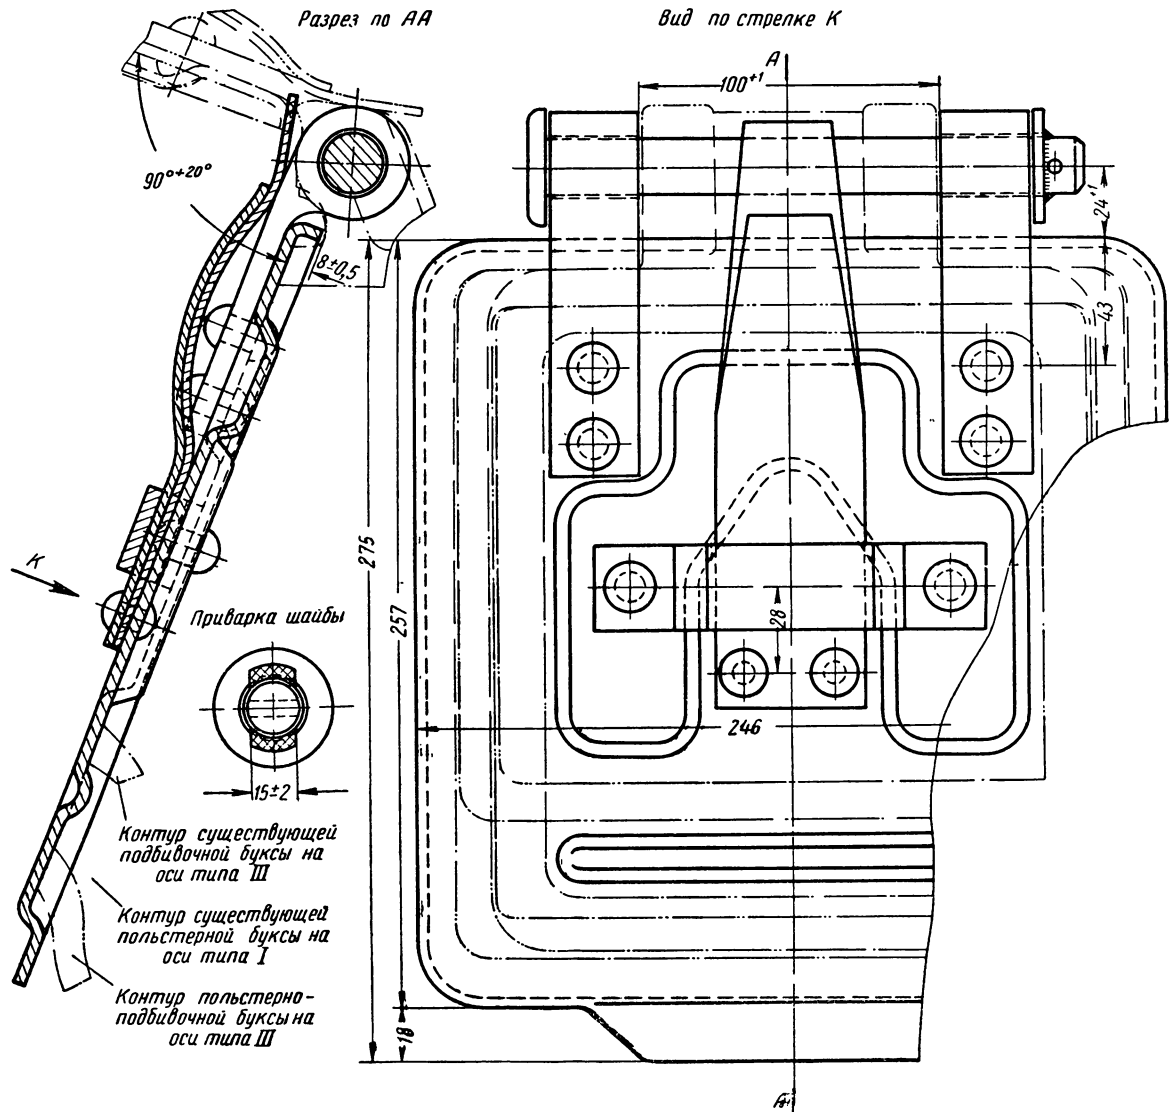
Буксовая крышка с двухлепестковой пружиной.
